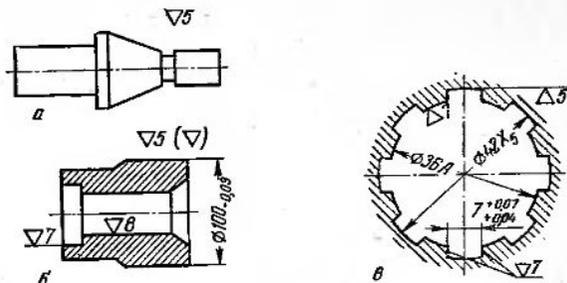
Примеры нанесения на чертежах обозначений шероховатости поверхности.
